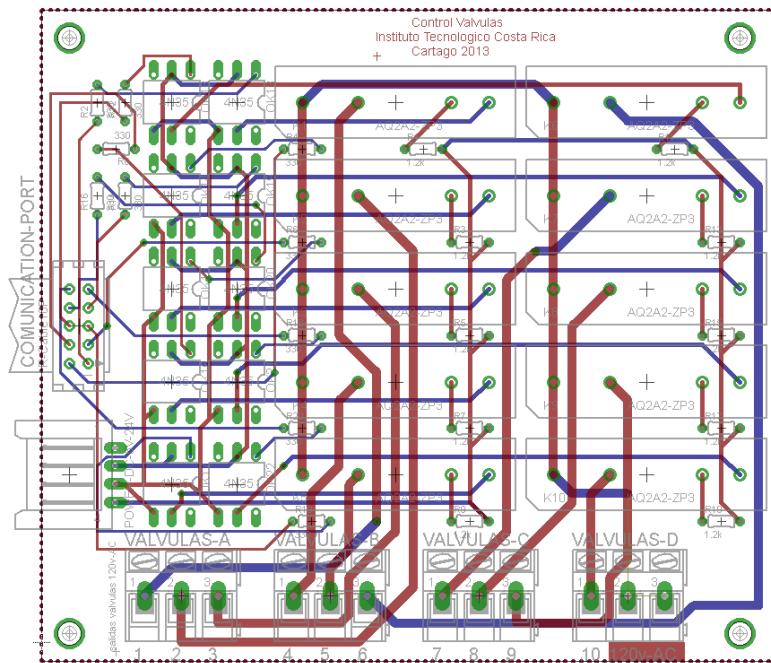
Placa PCB completa circuito salidas actuadores
